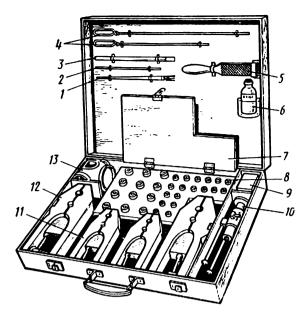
Lot d'outils et de dispositifs pour le soudage aluminothermique des brins de 16 à 240 mm² de section:
